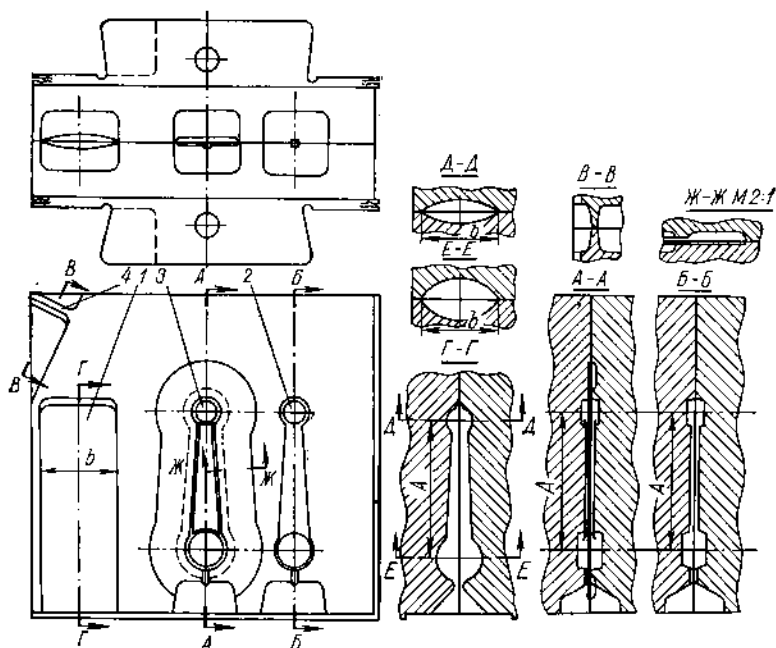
Многооручевой штамп для штамповки поковки шатуна от прутка
